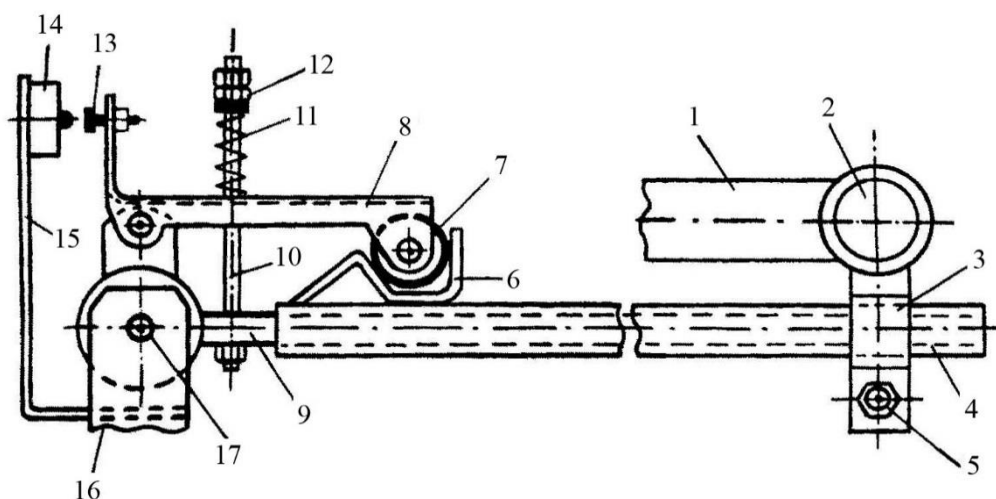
Схема механизма реверса привода дверей с разрывной телескопической штангой:
